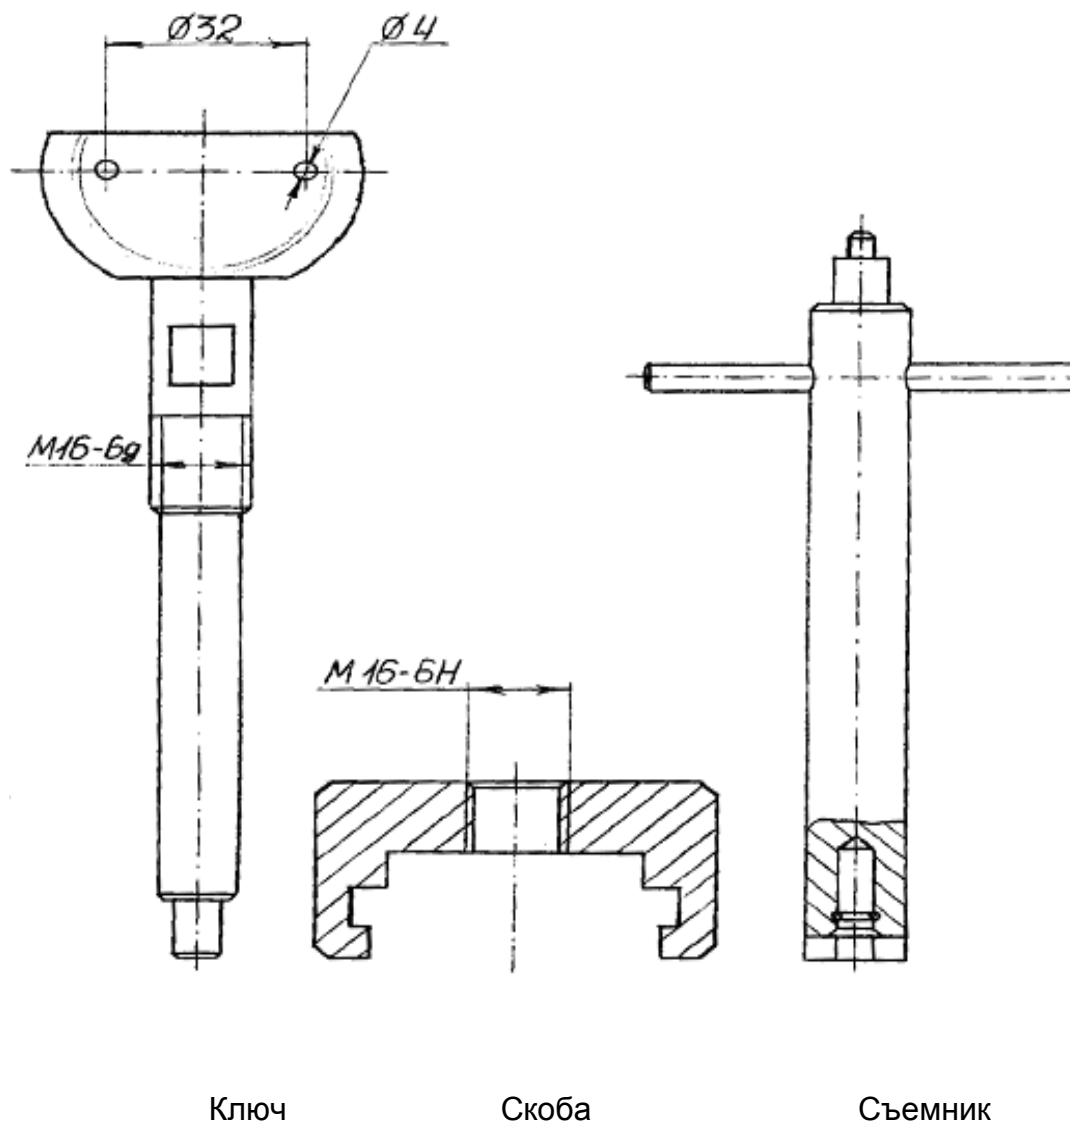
Инструмент для обслуживания сепаратора
